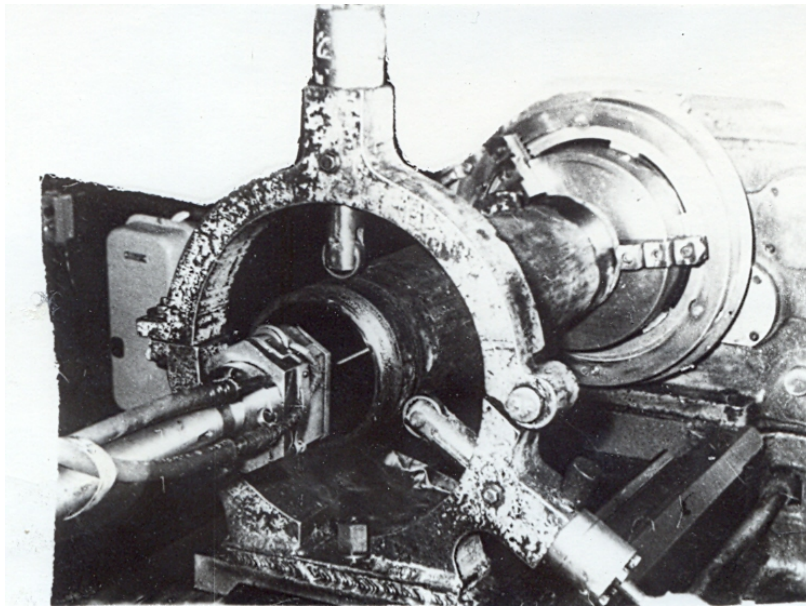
Опытная установка электромеханической обработки цилиндров (Рутченковский завод «Гормаш»)
